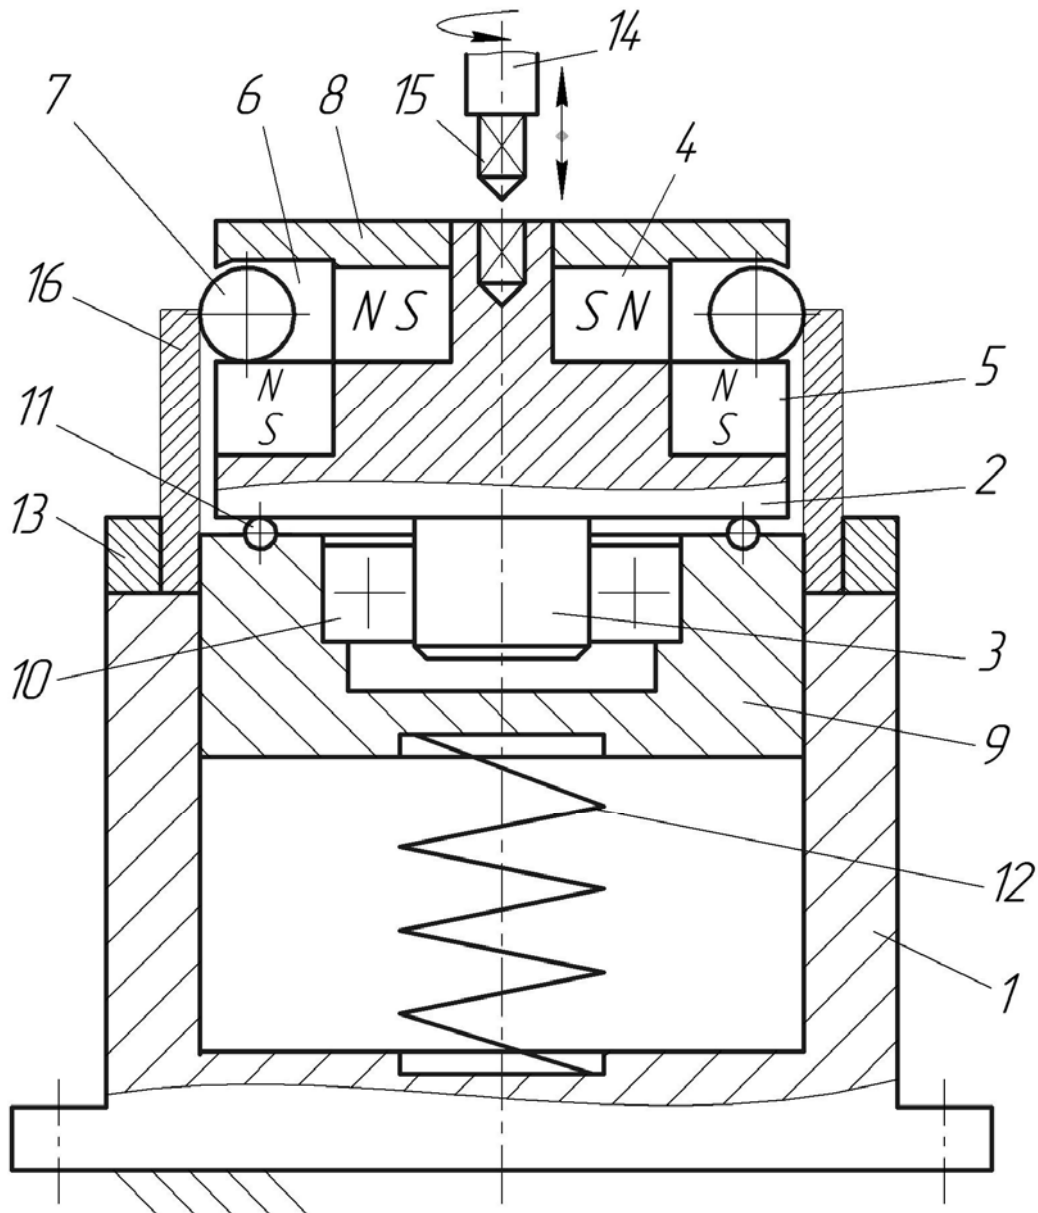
Схема совмещенного магнитно-вибродинамического упрочнения внутренней поверхности втулок на вертикально-сверлильном станке: 1 – цилиндрический корпус; 2 – ротор; 3 – шейка; 4, 5 – источники магнитного поля; 6 – кольцевая камера; 7 – деформирующие шары; 8 – шайба; 9 – плунжер; 10 – подшипник; 11 – шариковые опоры; 12 – пружина; 13 – упругое кольцо; 14 – поводковый центр; 15 – рабочий элемент поводкового центра; 16 – упрочняемая ферромагнитная втулка
